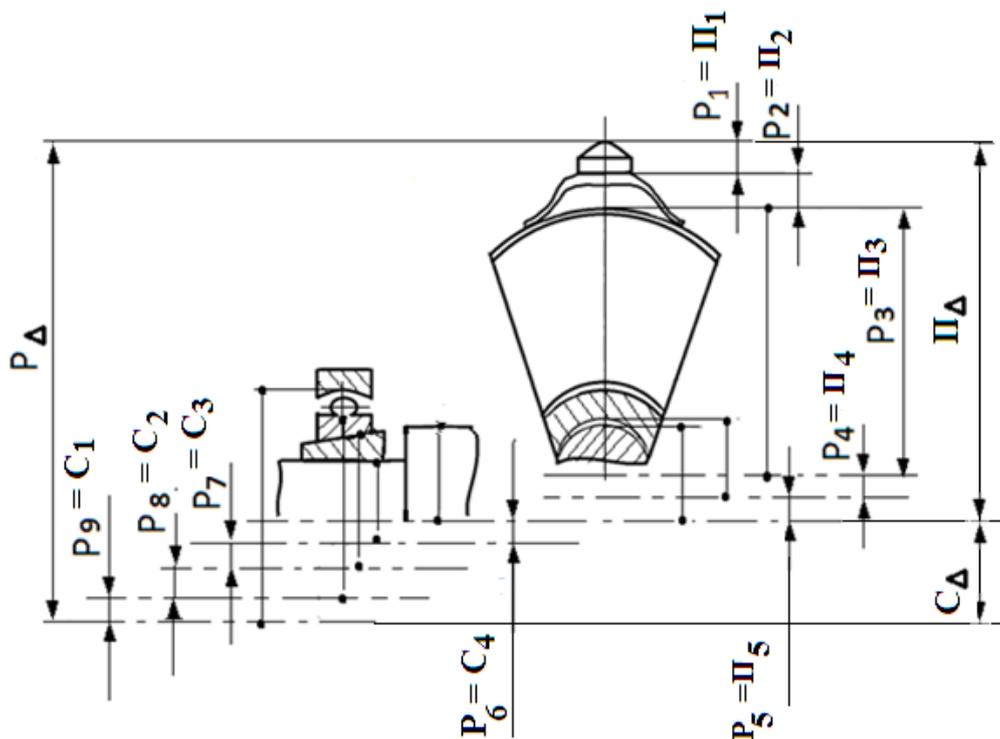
Размерная цепь формирования радиуса расположения вершин рабочего профиля бичей
